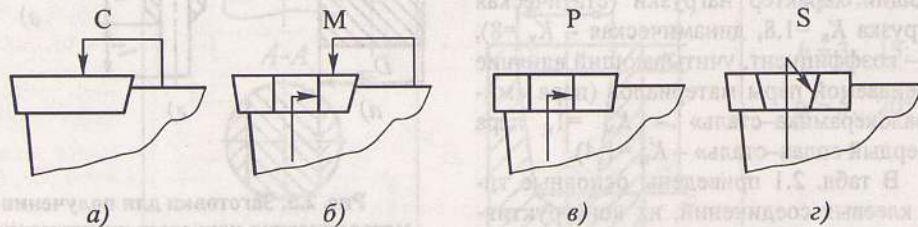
Схемы крепления СМП: а – прихватом сверху;
